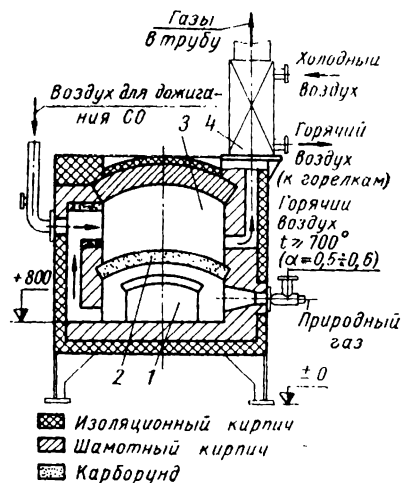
Малая рекуперативная камерная газовая печь для безокислительного нагрева стальных заготовок открытым пламенем: 1 — нижняя — рабочая камера; 2 — карборундовый свод; 3 — камера дожигания; 4 — жароупорный рекуператор [22]
